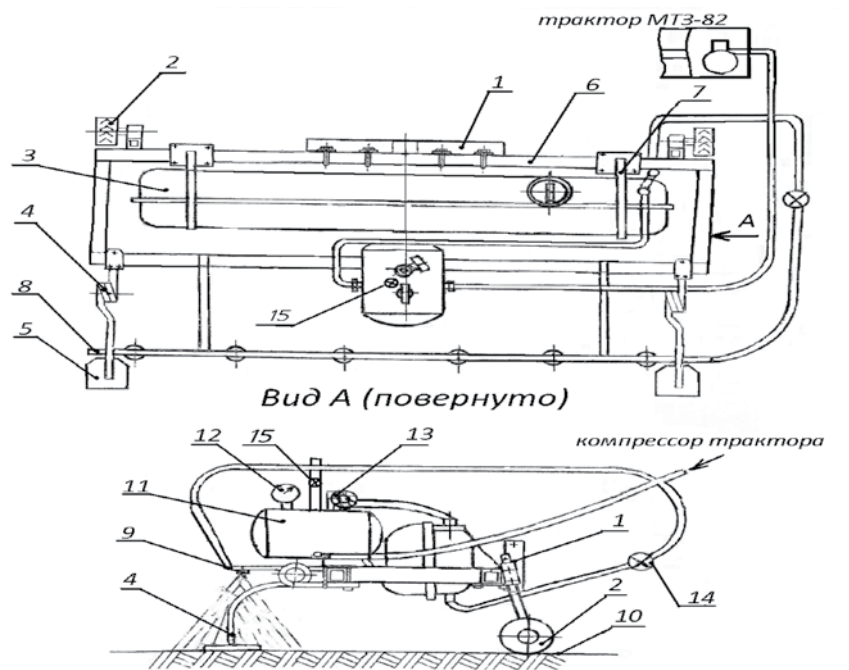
Принципиальная схема машины для внесения жидких удобрений на горные луга и пастбища: 1 – замок автосцепки; 2 – опорные колеса; 3 – цистерна; 4 – пружинистая стойка; 5 – дополнительная опора; 6 – рама; 7 – кронштейн крепления цистерны; 8 – коллектор распылителей; 9 – распылитель; 10 – почва; 11 – ресивер; 12 – манометр; 13 – клапан редуцирующий; 14 – кран управления, 15 – кран спуска воздуха
